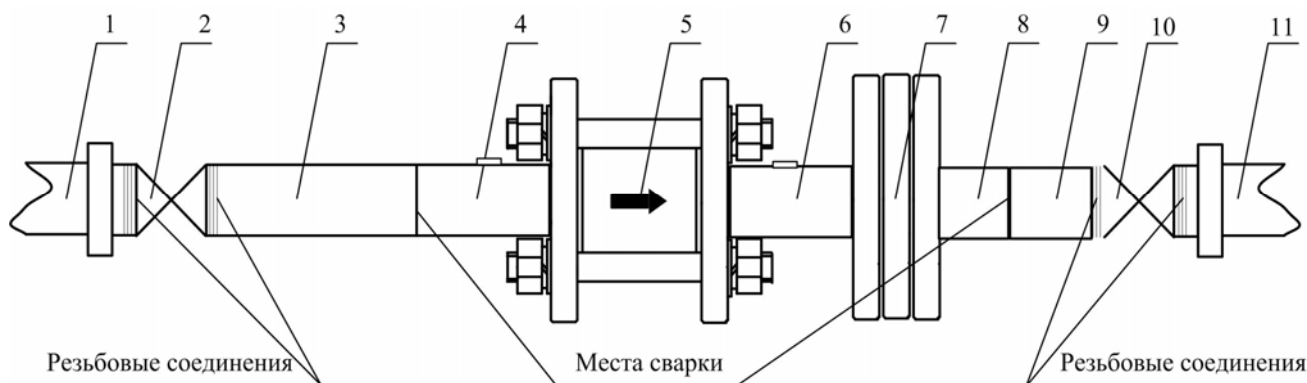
Вариант сборно-сварной конструкции с шаровыми задвижками.
